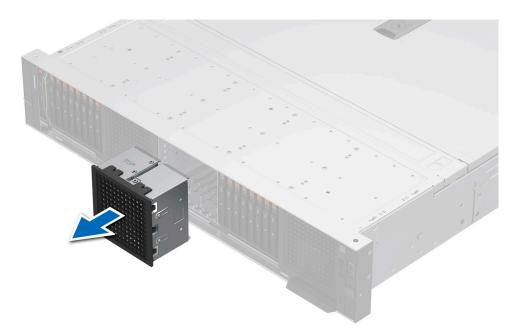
Entfernen des Platzhalters für ein E3.S-Laufwerksgehäuse
